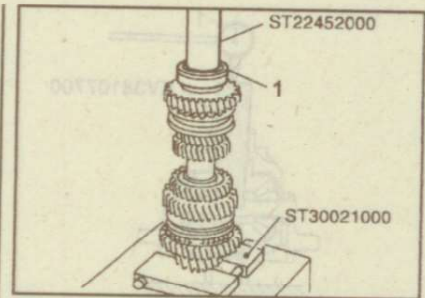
Установка заднего подшипника (1) вторичного вала
